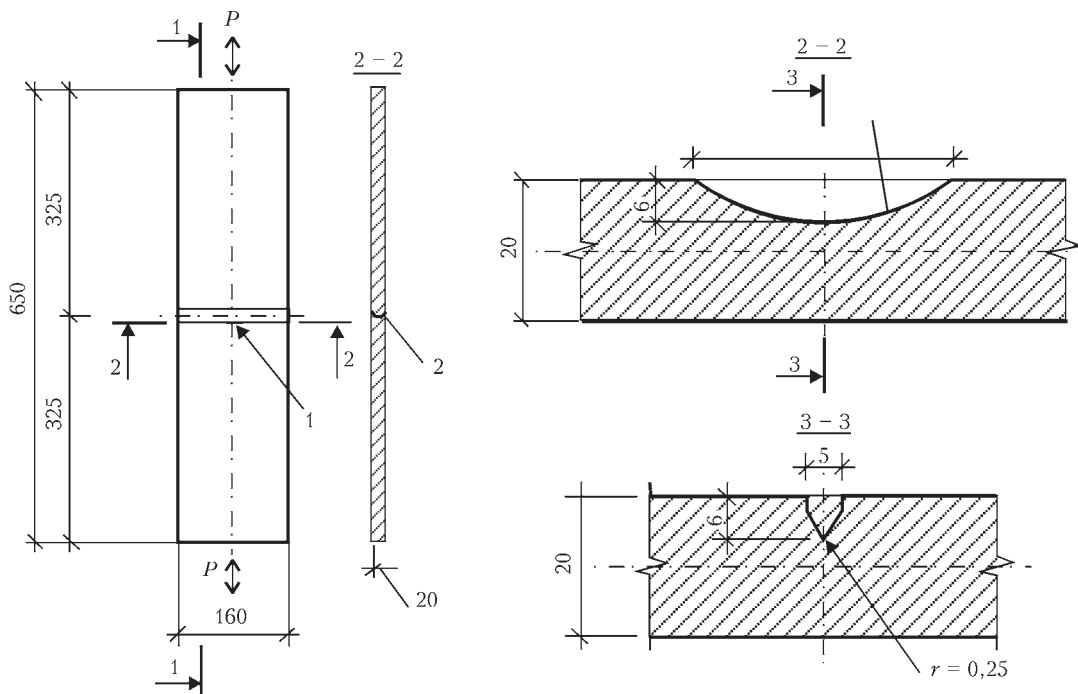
Схема и размеры образцов для испытания сварного соединения стали 09Г2СЮч-У390 на циклическую трещиностойкость; надрез по линии сплавления; усиление снято с двух сторон
